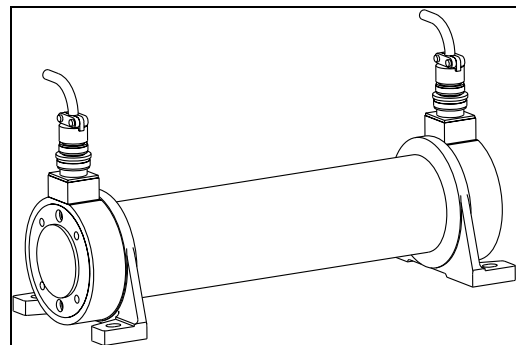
Einbau mit Lagerböcken bei „Ausseneinbau“ L000012
